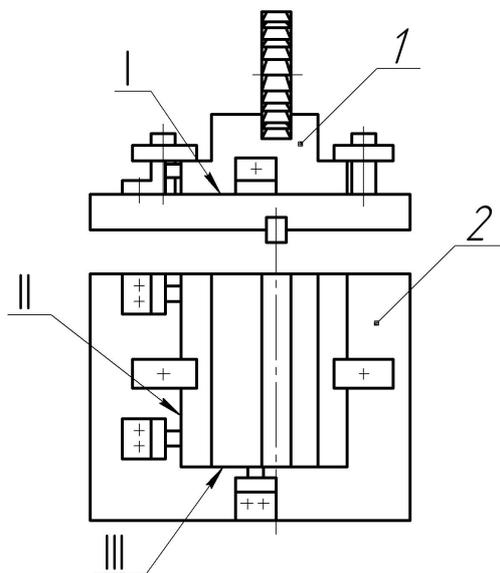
Схема к определению технологической базы: I, II, III – комплект технологических баз, определяющих положение заготовки в приспособлении; 1 – заготовка; 2 – приспособление
